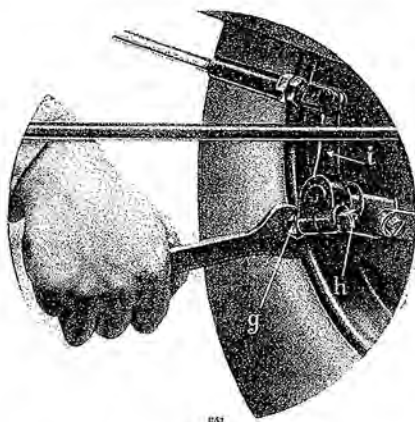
RÉGLAGE DU FREIN ARRIÈRE
